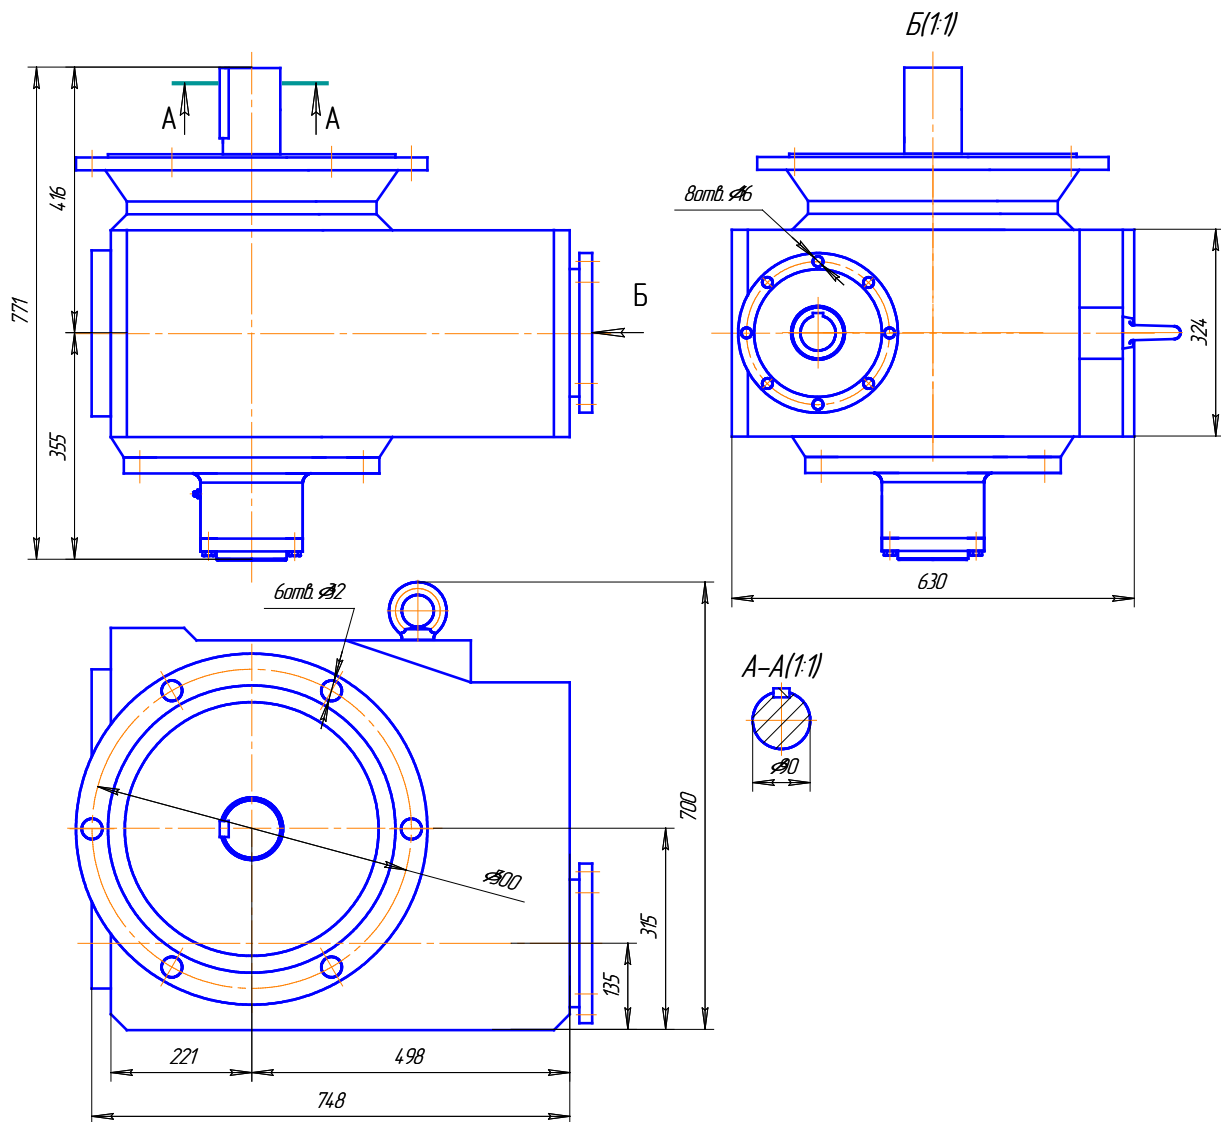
Ескіз черв'ячного редуктора типу B8 9052 фірми « NORD »
